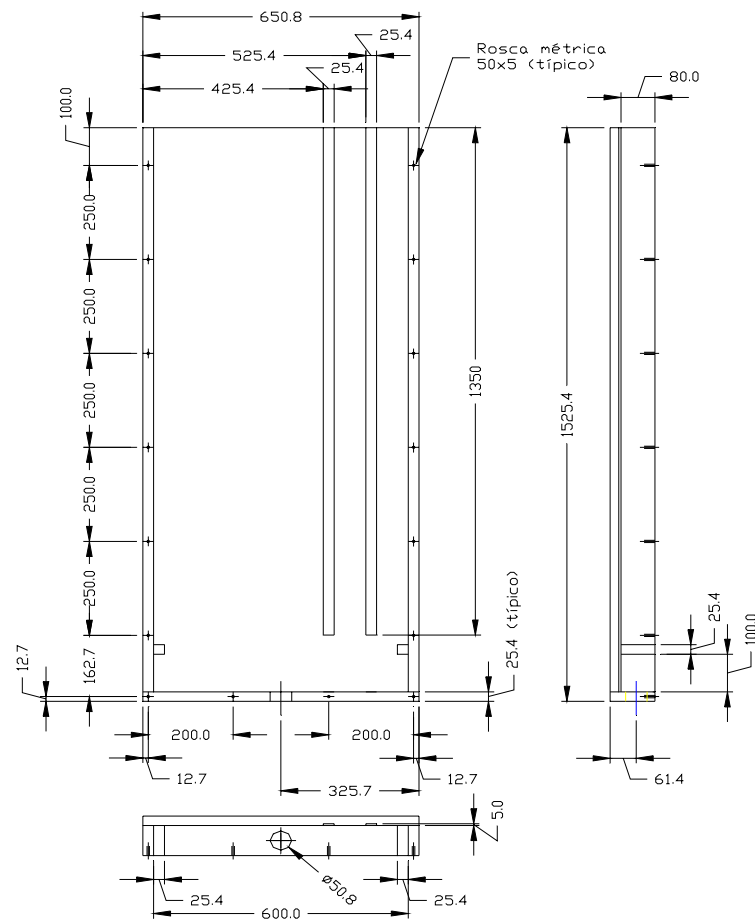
Vistas frontal, lateral e superior do molde, com as dimensões em milímetros.
